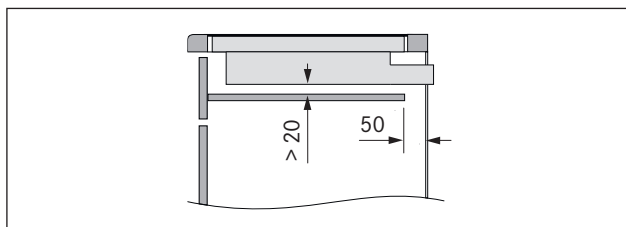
Vista laterale piano di protezione cavi e aerazione
